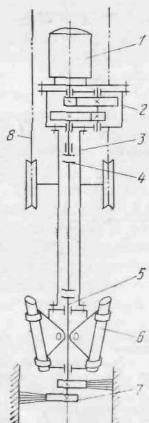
Кинематическая схема механизма для чистки сквозных изложниц
